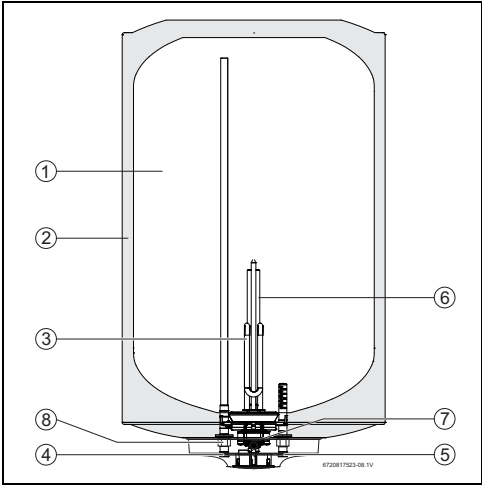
Конструкция бака (здесь: Tronic 2000 T)
